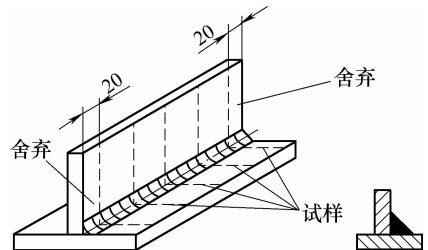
板材角焊缝试件金相试样（宏观）截取位置
